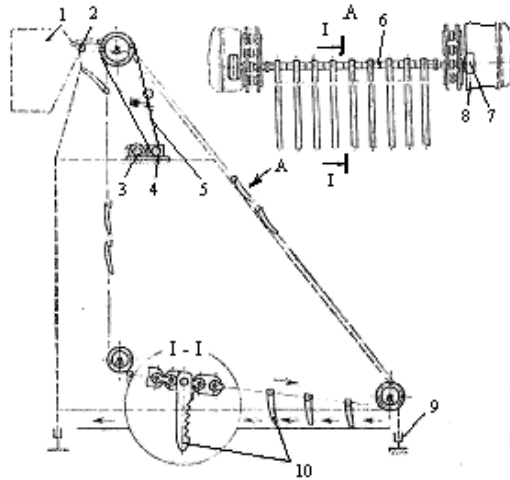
Схема грабельно-ланцюгового соломовловлювача: 1 – прий-мальник; 2 – ролик; 3 – електродвигун; 4 – редуктор; 5 – ланцюгова передача; 6 – осі встановлення пластин; 7 – ролики; 8 – направляючі; 9 – регулювальні гвинти; 10 – пластини
